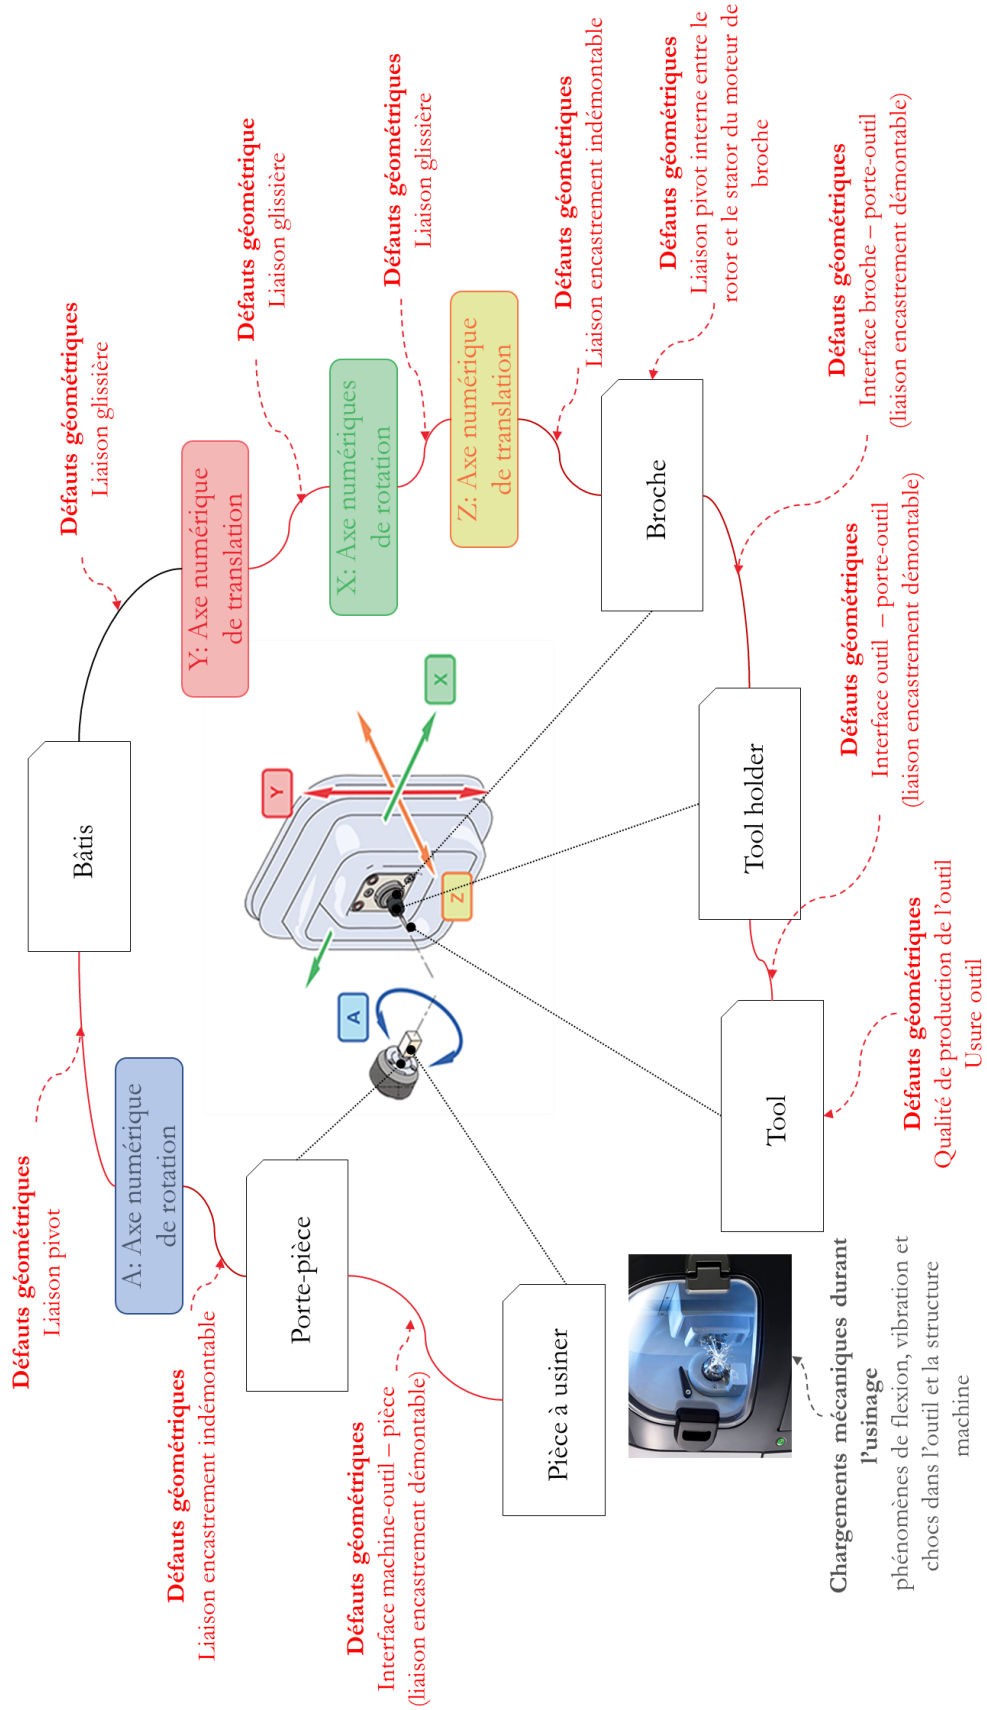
Structure d'une machine-outil : sources de dispersions géométriques (exemple basé sur la machine-outil Carestream CS 3000, Carestream dental [New York, USA])
